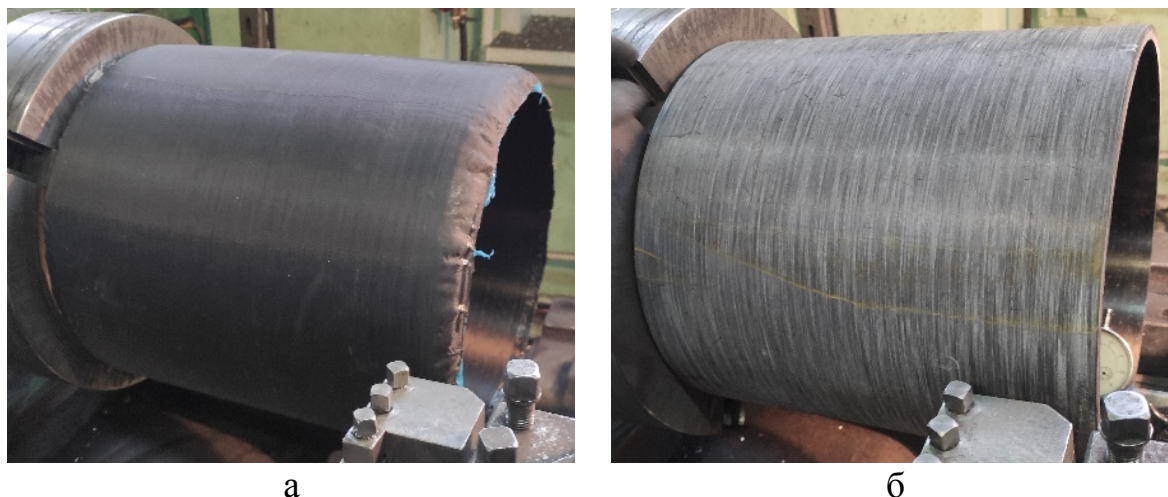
Фотография заготовки до (а) и после (б) механической обработки
